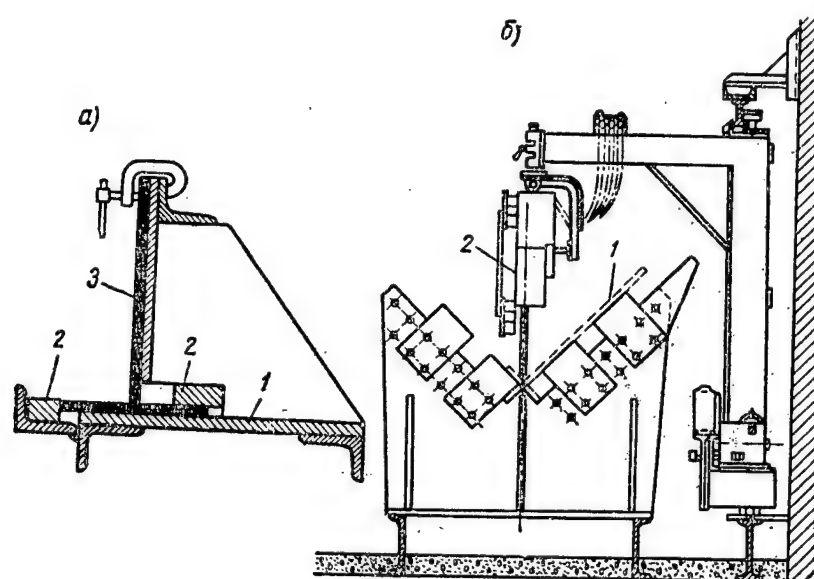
Сборка и сварка балки таврового сечения:
